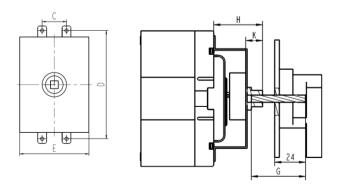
Габаритные и установочные размеры ручки на дверь шкафа РП-300, мм
